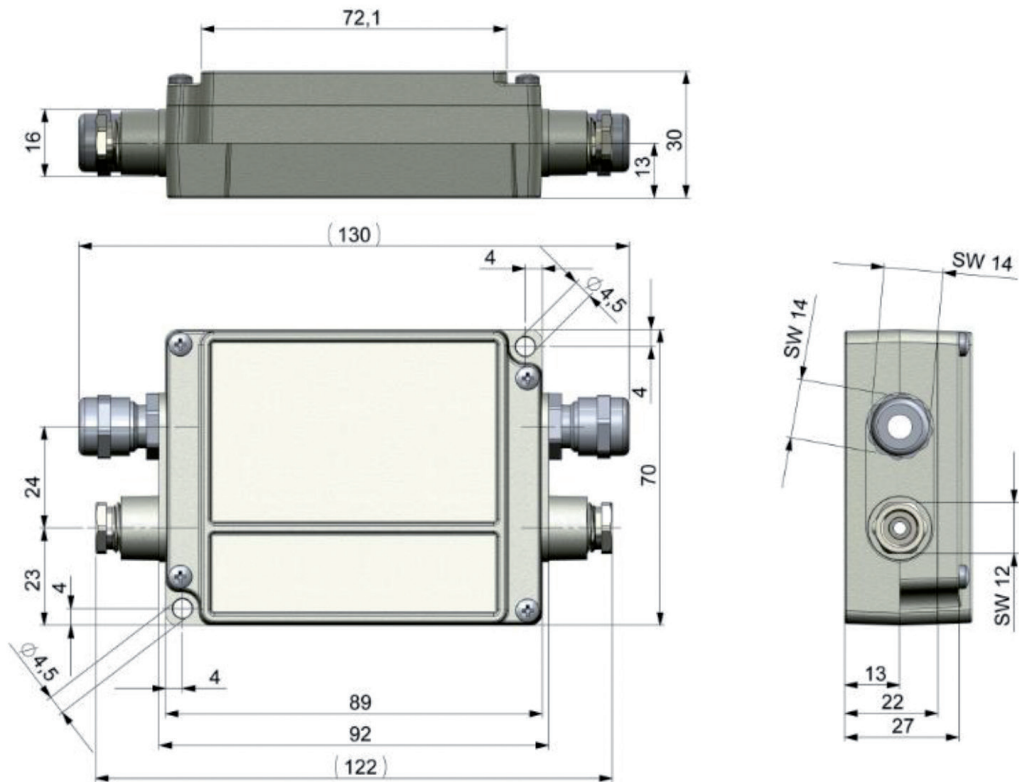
Industrielles/stackable PIF (Prozess-Interface) - Elektronikbox, Steuerbox Shutter, Abmessungen in mm
